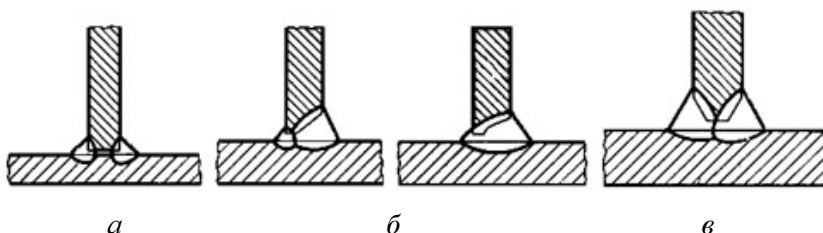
Подготовка кромок угловых швов тавровых соединений
